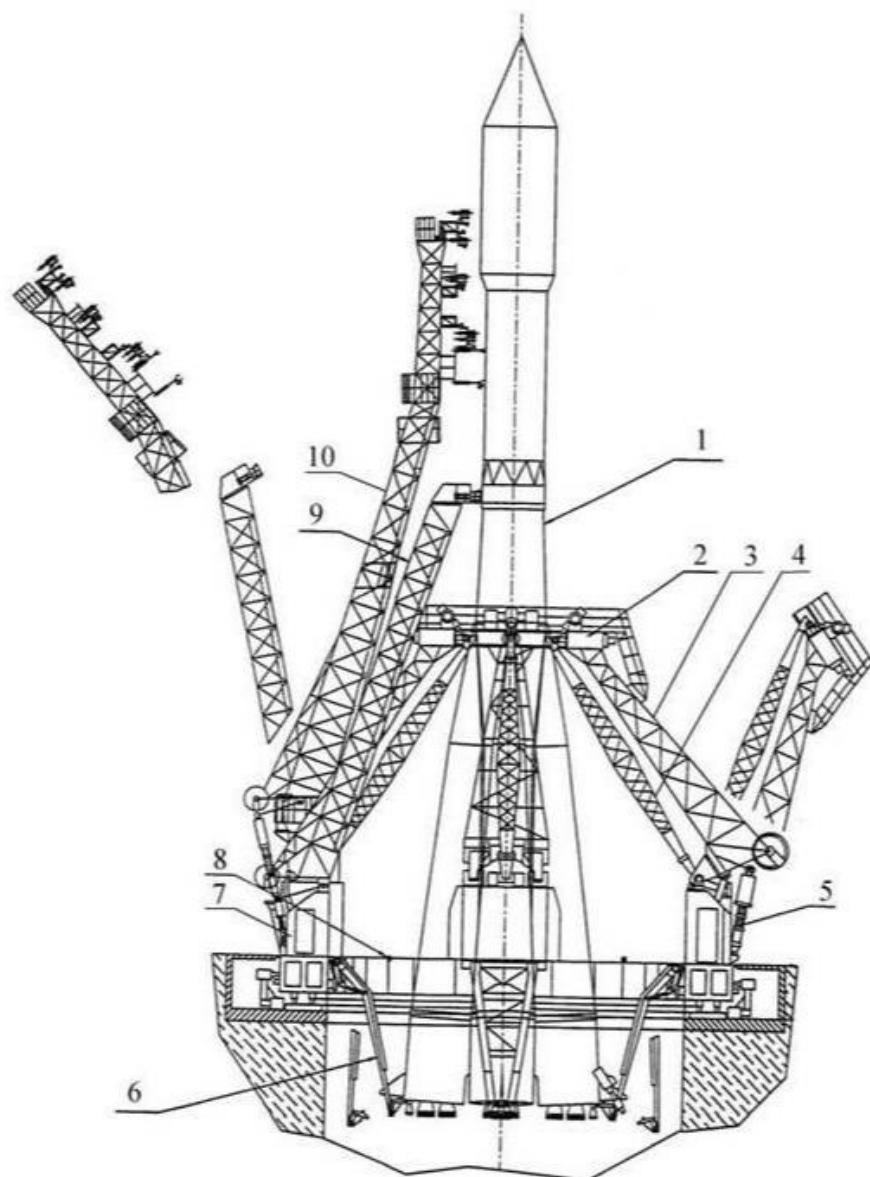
Схема ферм СС, где 1 – РКН, 2 – верхний силовой пояс, 3 – фермы – опоры, 4 – несущие стрелы, 5 – гидравлические буферы, 6 – НУ, 7 – основание ферм – опор, 8 – кольцо опорное, 9 – ВКМ, 10 – КЗМ
